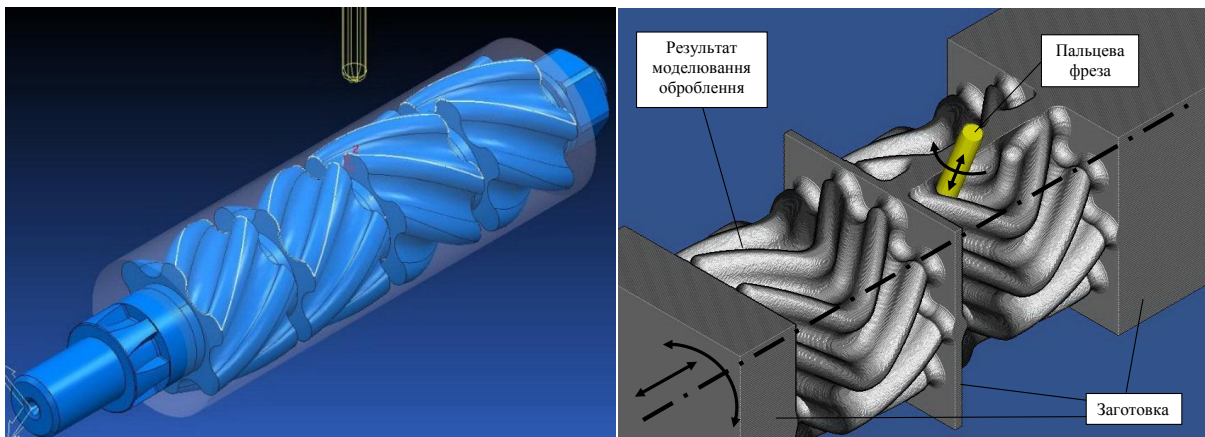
Комп'ютерна імітація фрезерування зубчастих коліс в Autodesk PowerMill
